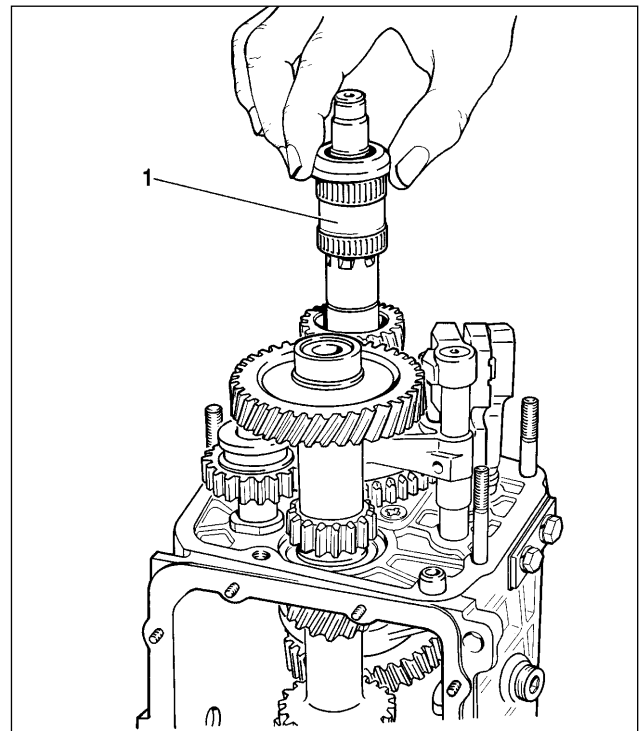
Ausbau der Buchse des Zahnrads für 5. Gang:
